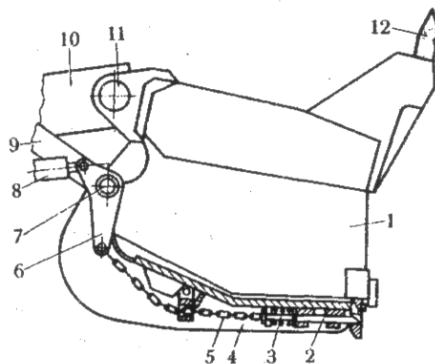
, Неповоротный ковш прямой лопаты экскаваторов ЭО-4124:
